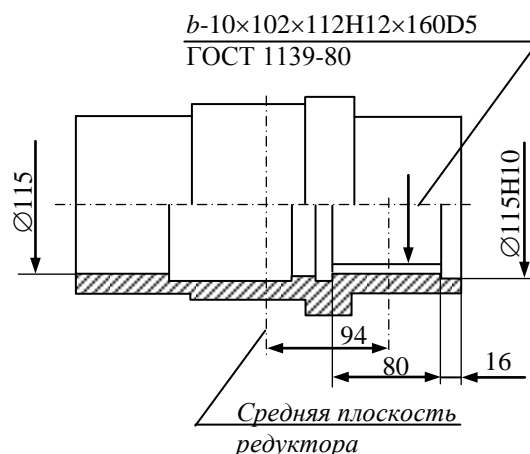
П7 Присоединительные размеры вала редуктора 1Ц2У-2500
